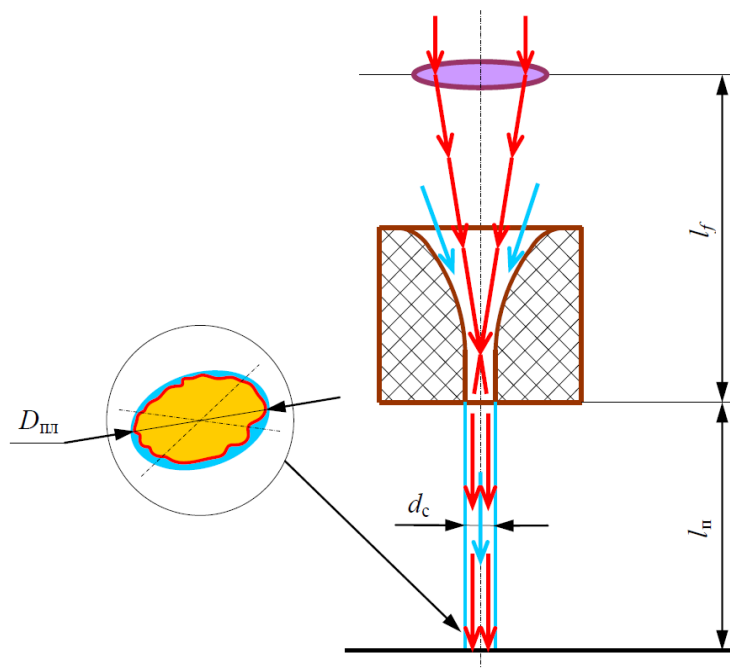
Вплив струминно-лазерного променя на оброблювану поверхню
